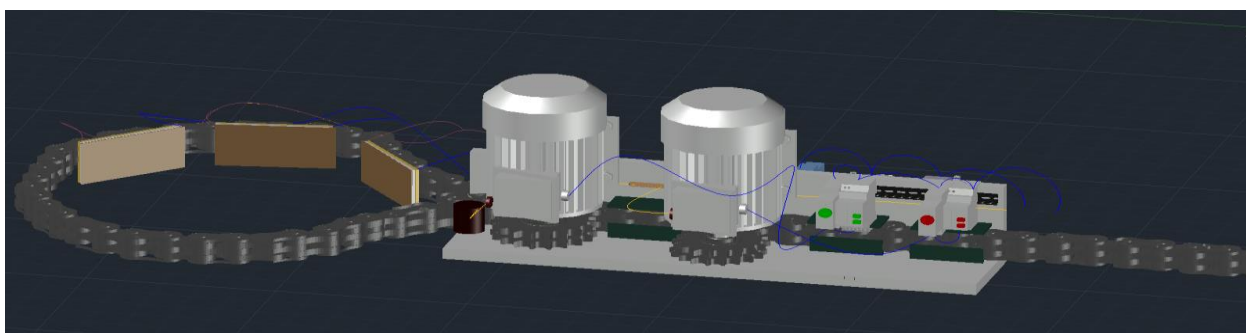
Готовое оборудование для спайки биг-бэг мешка (вид слева)
